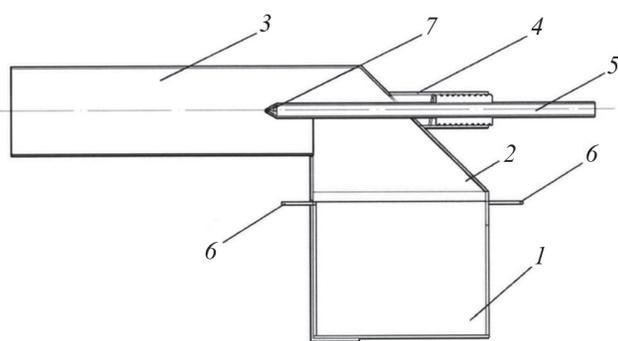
Конструктивная схема горелочного устройства [3, 4]:
